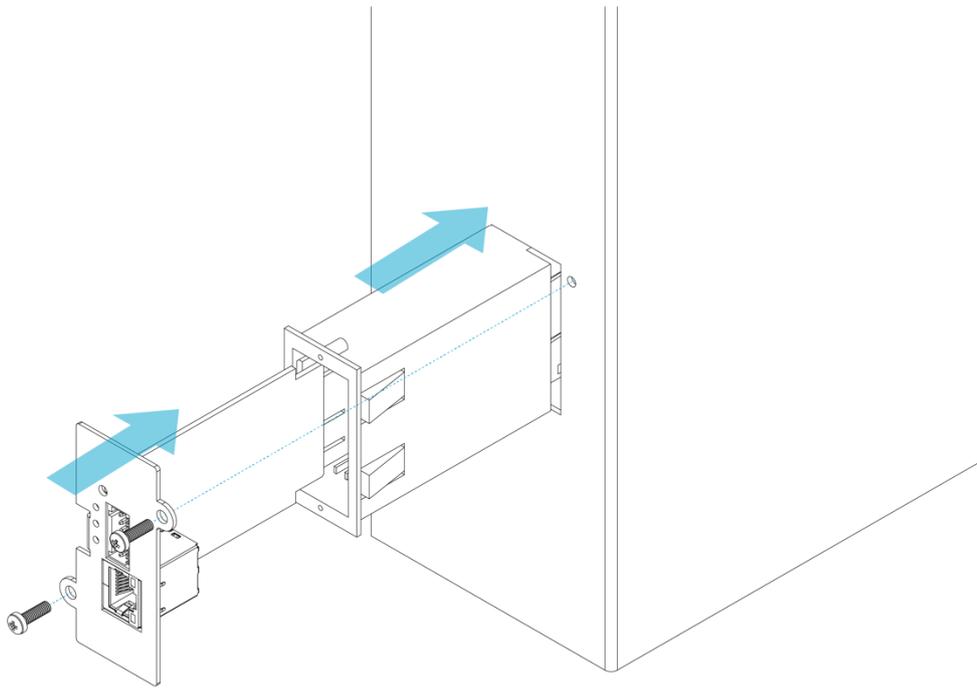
Установка устройства в ИБП RTMP II
